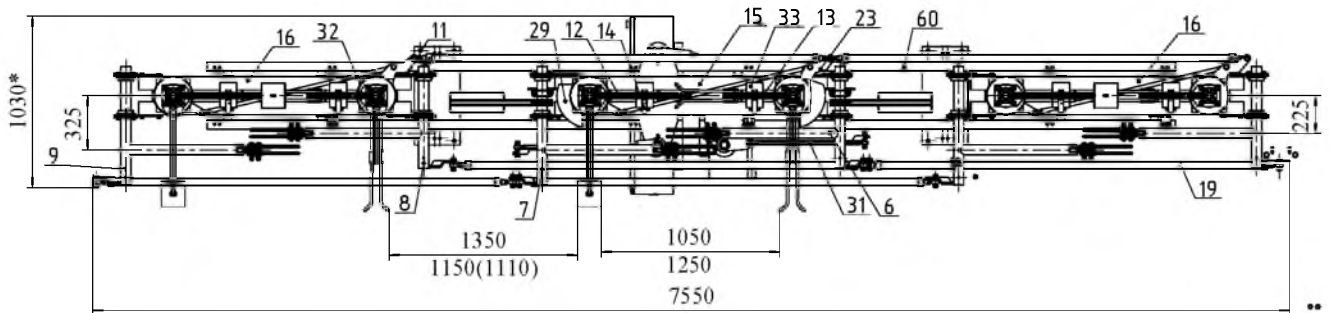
Общий вид разъединителя РН□К СЭЩ-□-□-110/□
